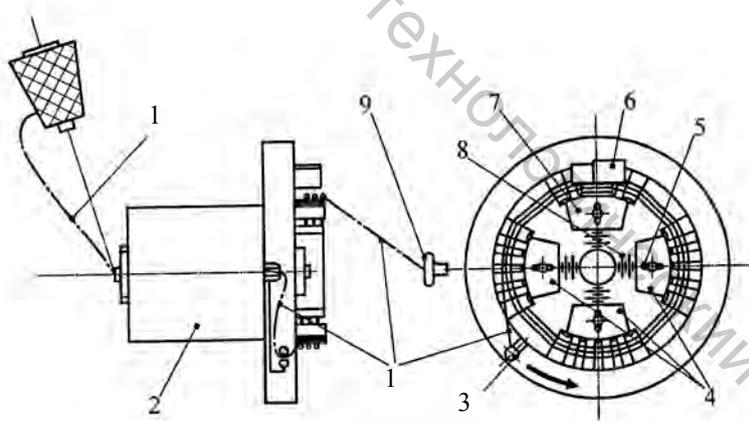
Отмеривающее устройство современного пневматического станка
